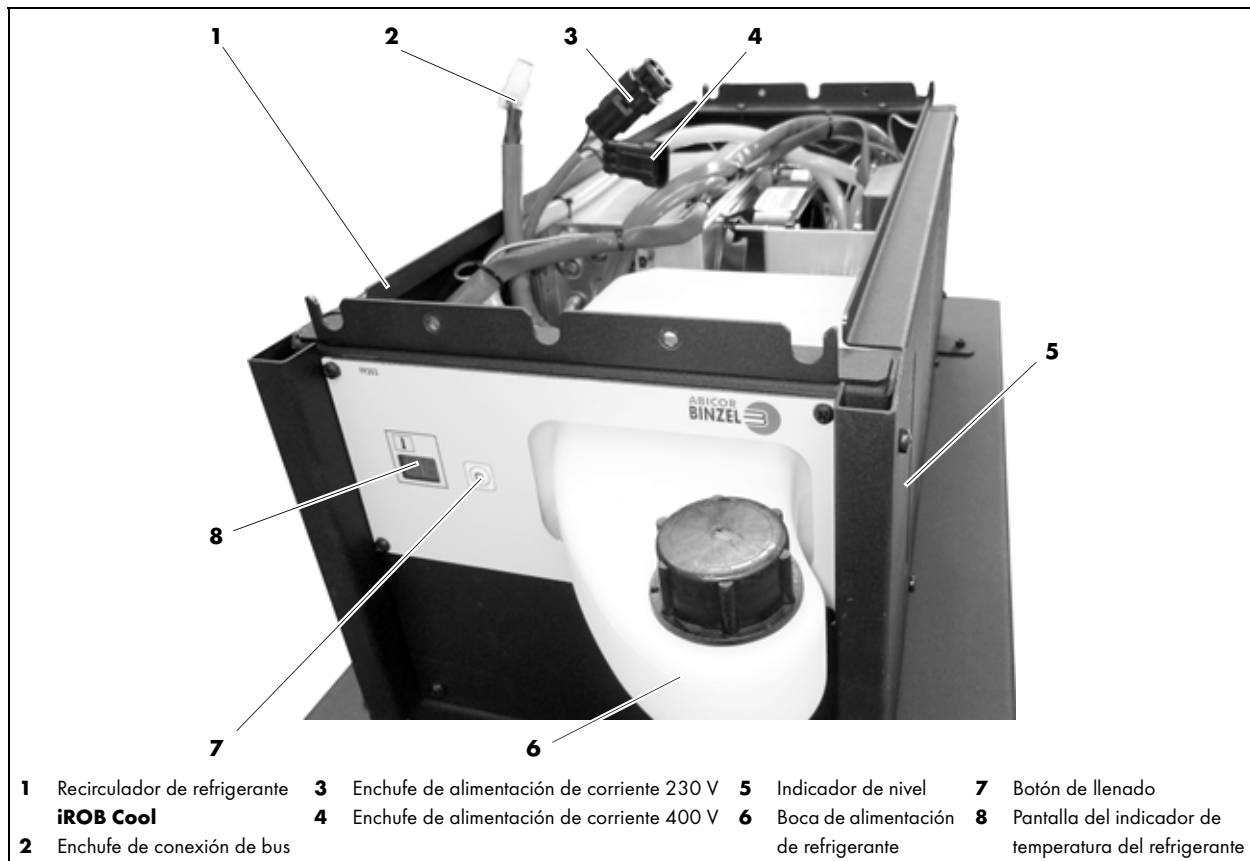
Componentes del recirculador de refrigerante iROB Cool
